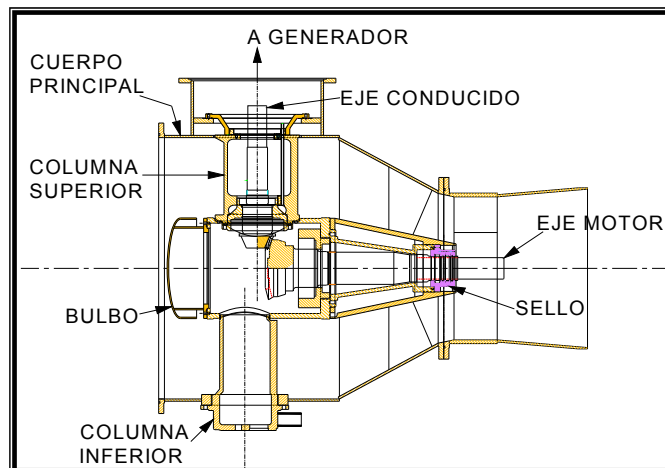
Vista del conjunto cuerpo principal de la turbomáquina.
